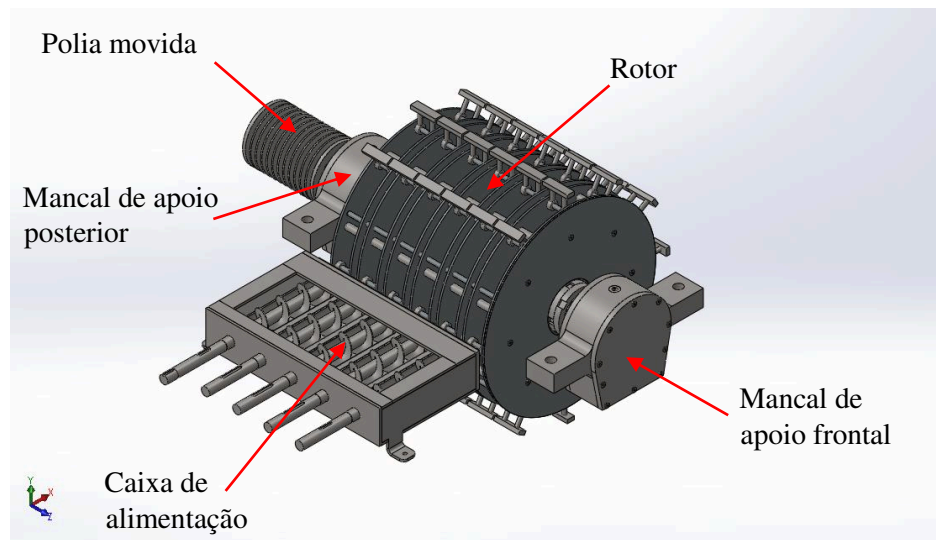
Pulverizador horizontal - Representação 3D no Solidworks.
